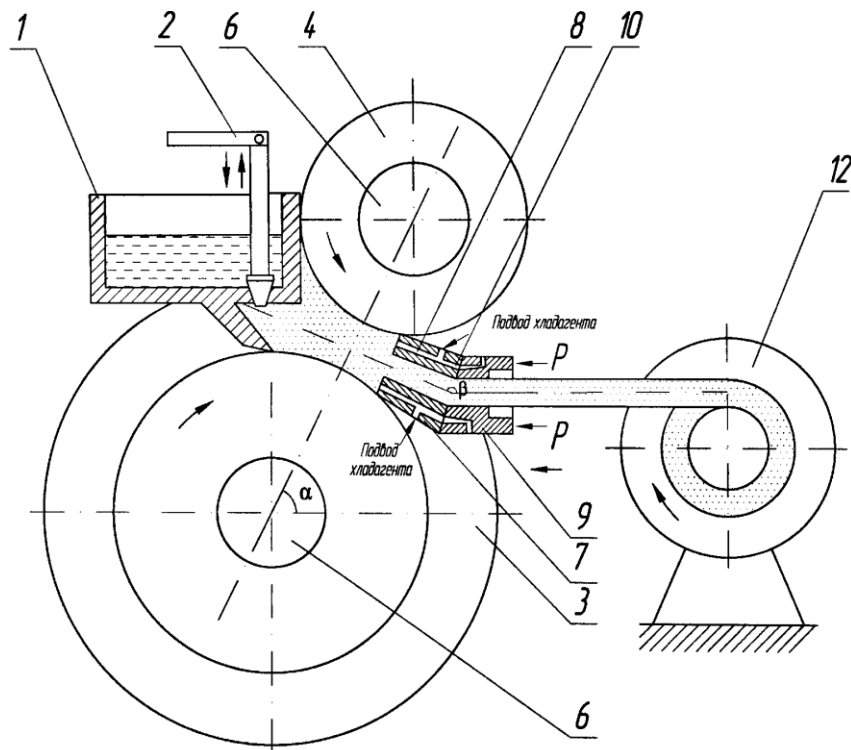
Устройство для непрерывного литья, прокатки и прессования
